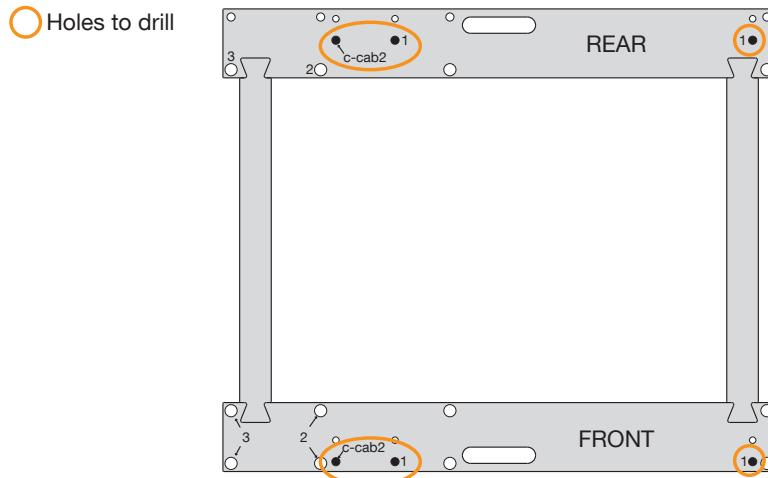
Bohrungen für die Installation von 1 C-Cab + 1 C-Cab Extension
